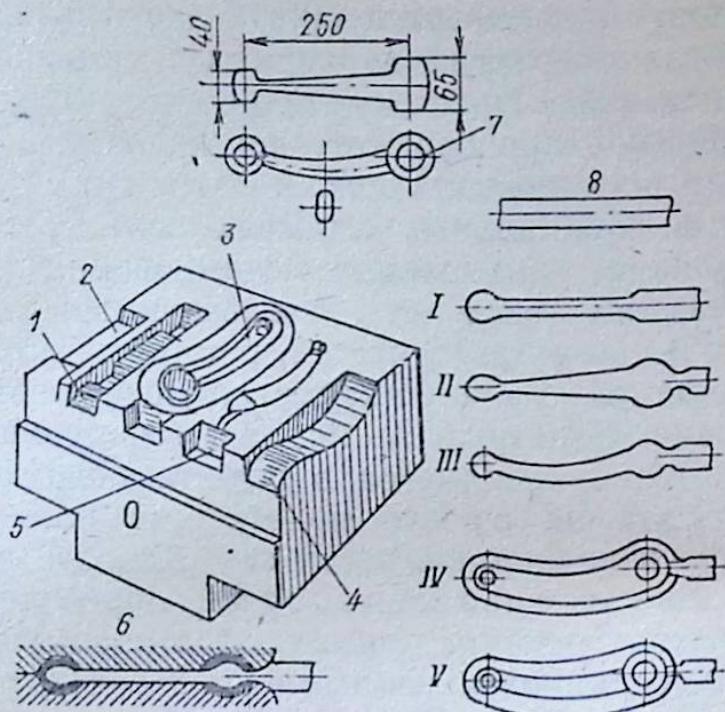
Многоручьевый молотовый штамп и операции штамповки шатуна:
